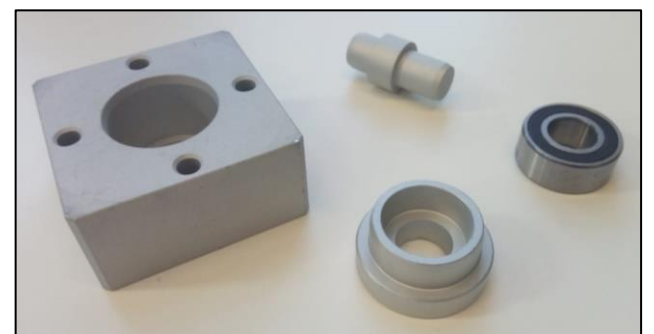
Vier Bauteile: Block, Achse, Deckel, Lager (v.l.n.r.)
